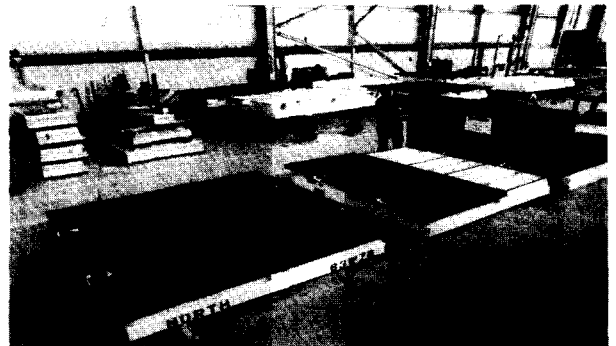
Mechlite 제작 장면(Mech-Tool Engineering 사).
